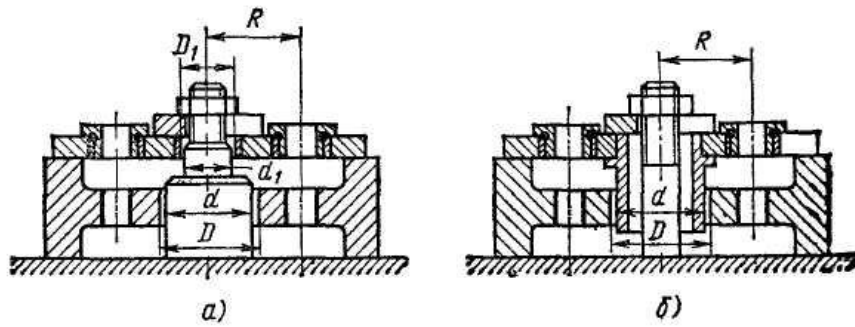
Схема базування і розрахунку затискних зусиль при обробці заготовок на свердлильних верстатах в накладному кондукторі
